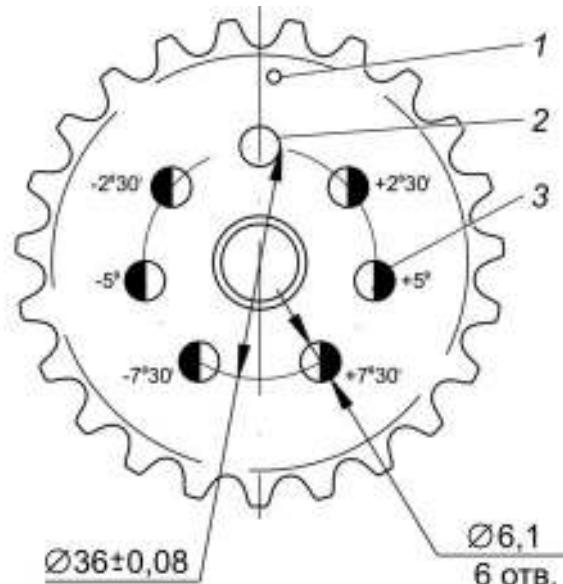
Звездочка распределительного вала с дополнительными отверстиями: 1 - метка; 2 - заводское отверстие; 3 - дополнительные отверстия.
